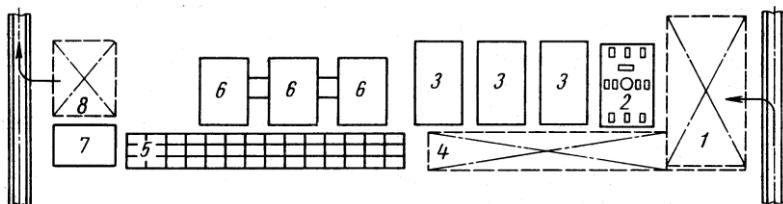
Технологическая схема участка сборки и сварки рамы экскаватора ЭГ-4,6.
